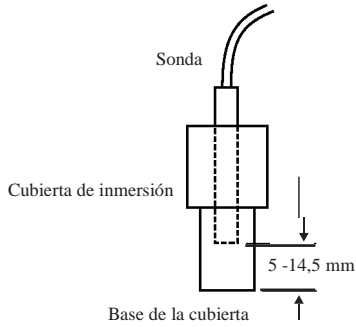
Montaje de la sonda con cubierta de inmersión
